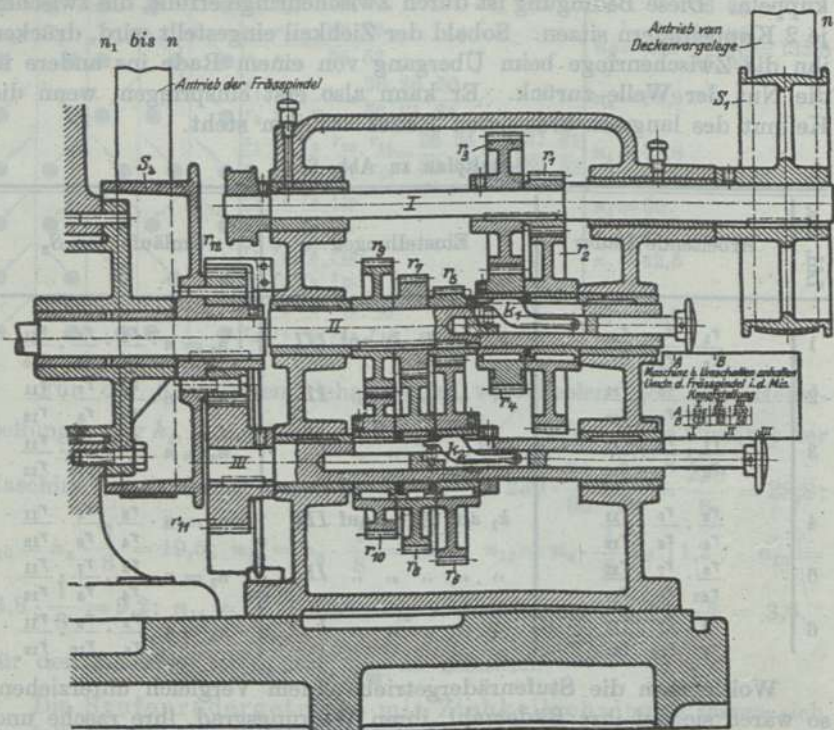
Stufenrädernetriebe mit Ziehkeilschaltung.
